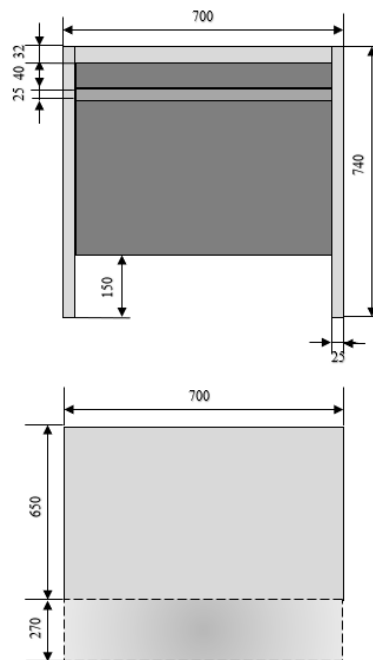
Croquis puesto de trabajo mesa principal trabajadora 7. Fuente: elaboración propia
